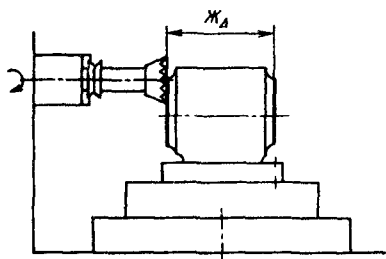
Схема получения размера между поверхностями, обработанными за один установ заготовки и режущего инструмента с поворотом стола станка на 180°
